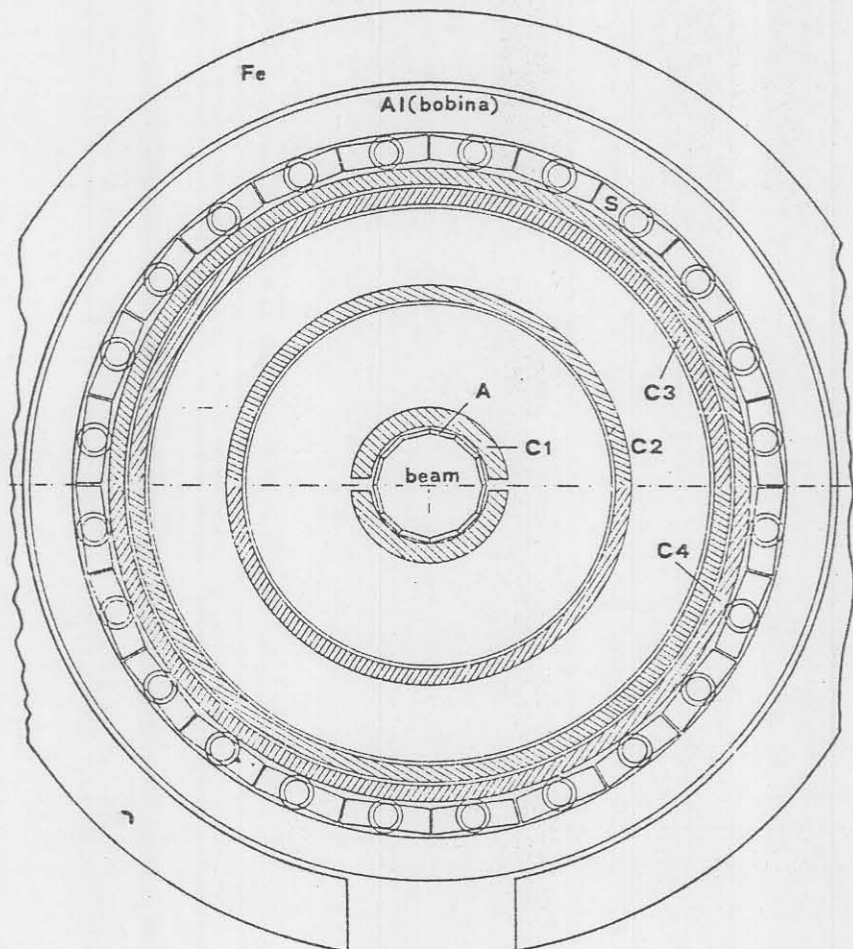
Vista frontale del dispositivo con campo longitudinale (MAL).
